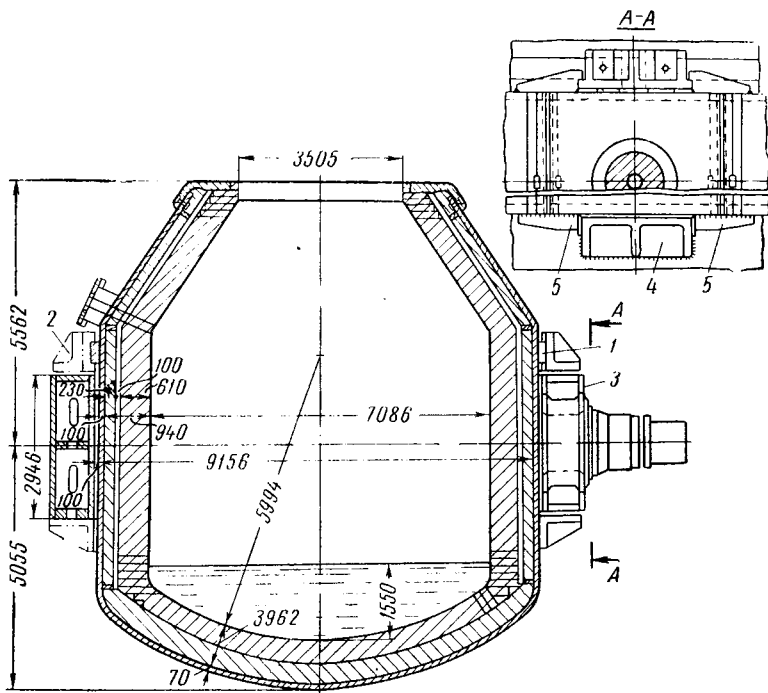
Конструкция и крепление 270-т кислородного конвертера:
